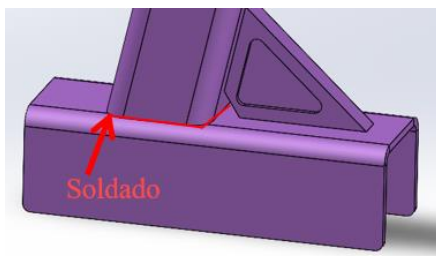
Vistas de soldado inferior de pieza N°1 (Fuente 84)
